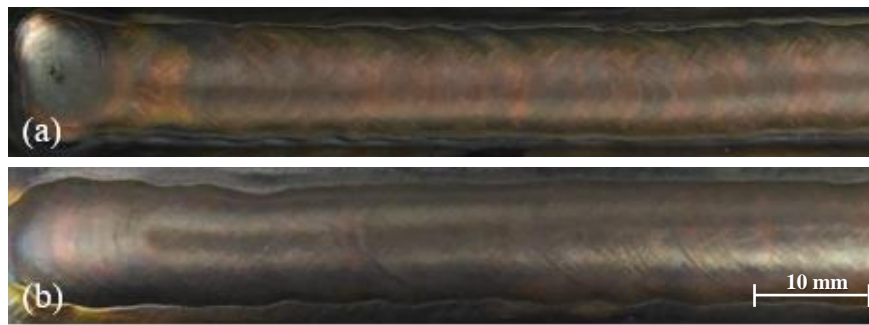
Aspecto superficial dos cordões soldados com as distâncias de (a) 0,5 mm e (b) 1 mm.
